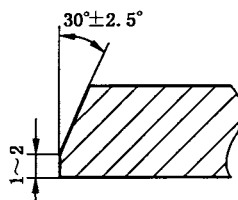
端管焊接连接端对接型焊接接头坡口
